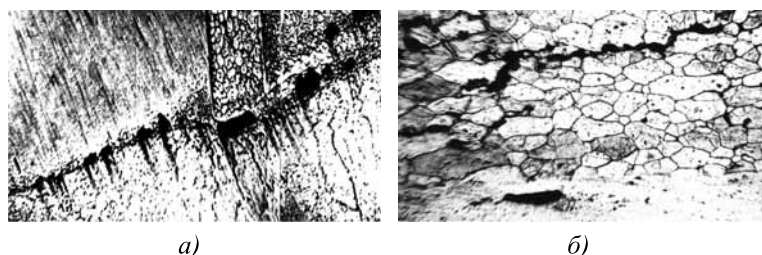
Поры (а) и трещины (б) по линии сплавления в сварном образце, выполненном ручной аргодуговой сваркой. $\times 68$
